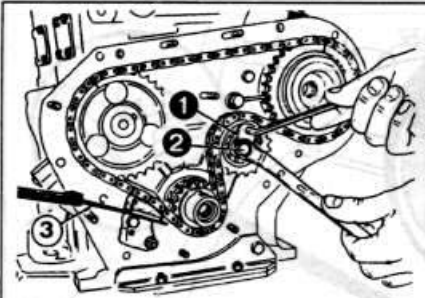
Регулировка натяжения цепи привода распределительного вала и ТНВД:
